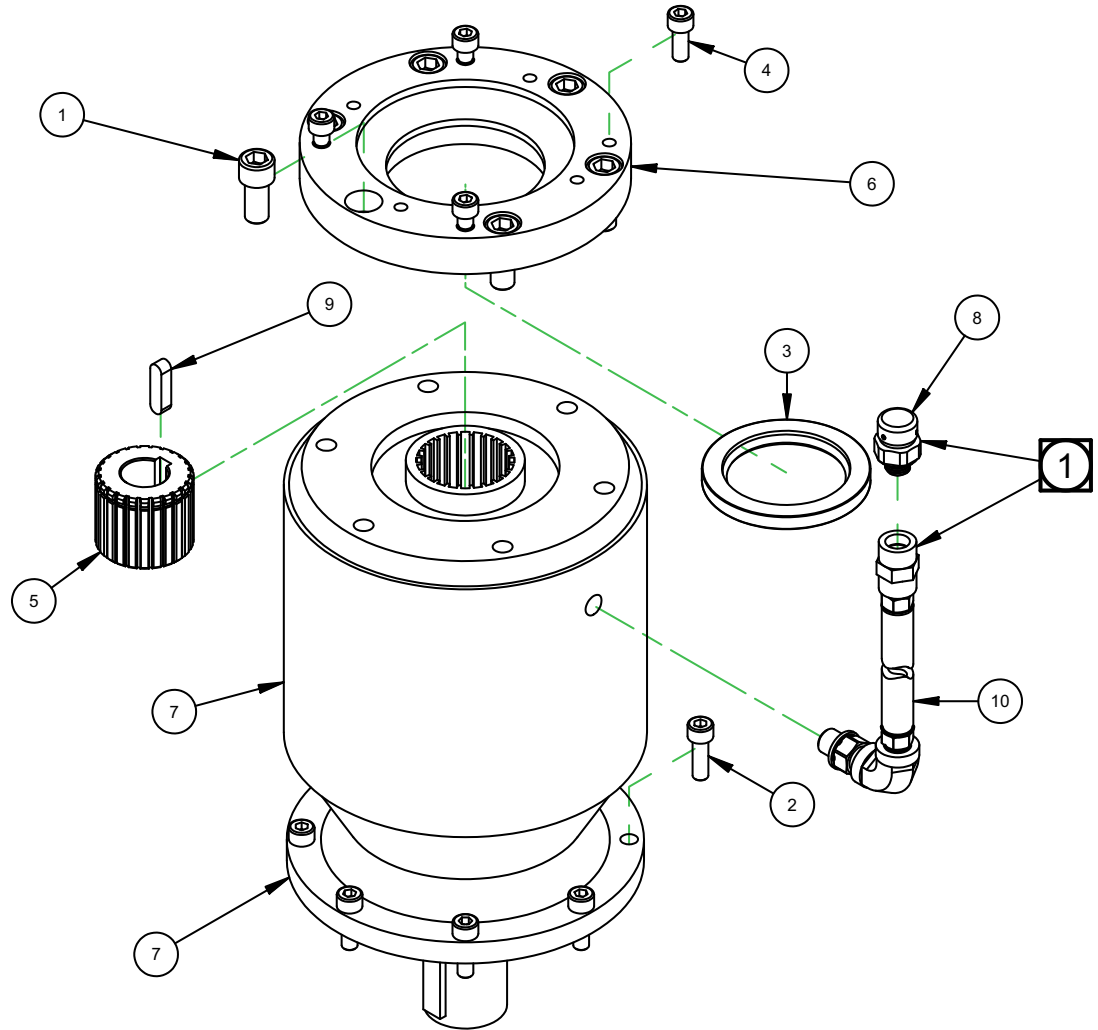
EXTENSION BLOC TÊTE DE FRAISAGE (P/N 65840)
